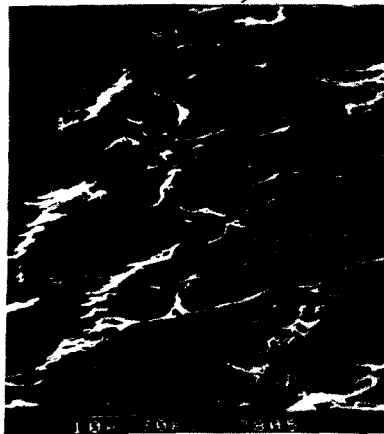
Bruchfläche einer PE-Stahl-Klebverbindung mit Epoxidharz, Schubspannungsbruch
